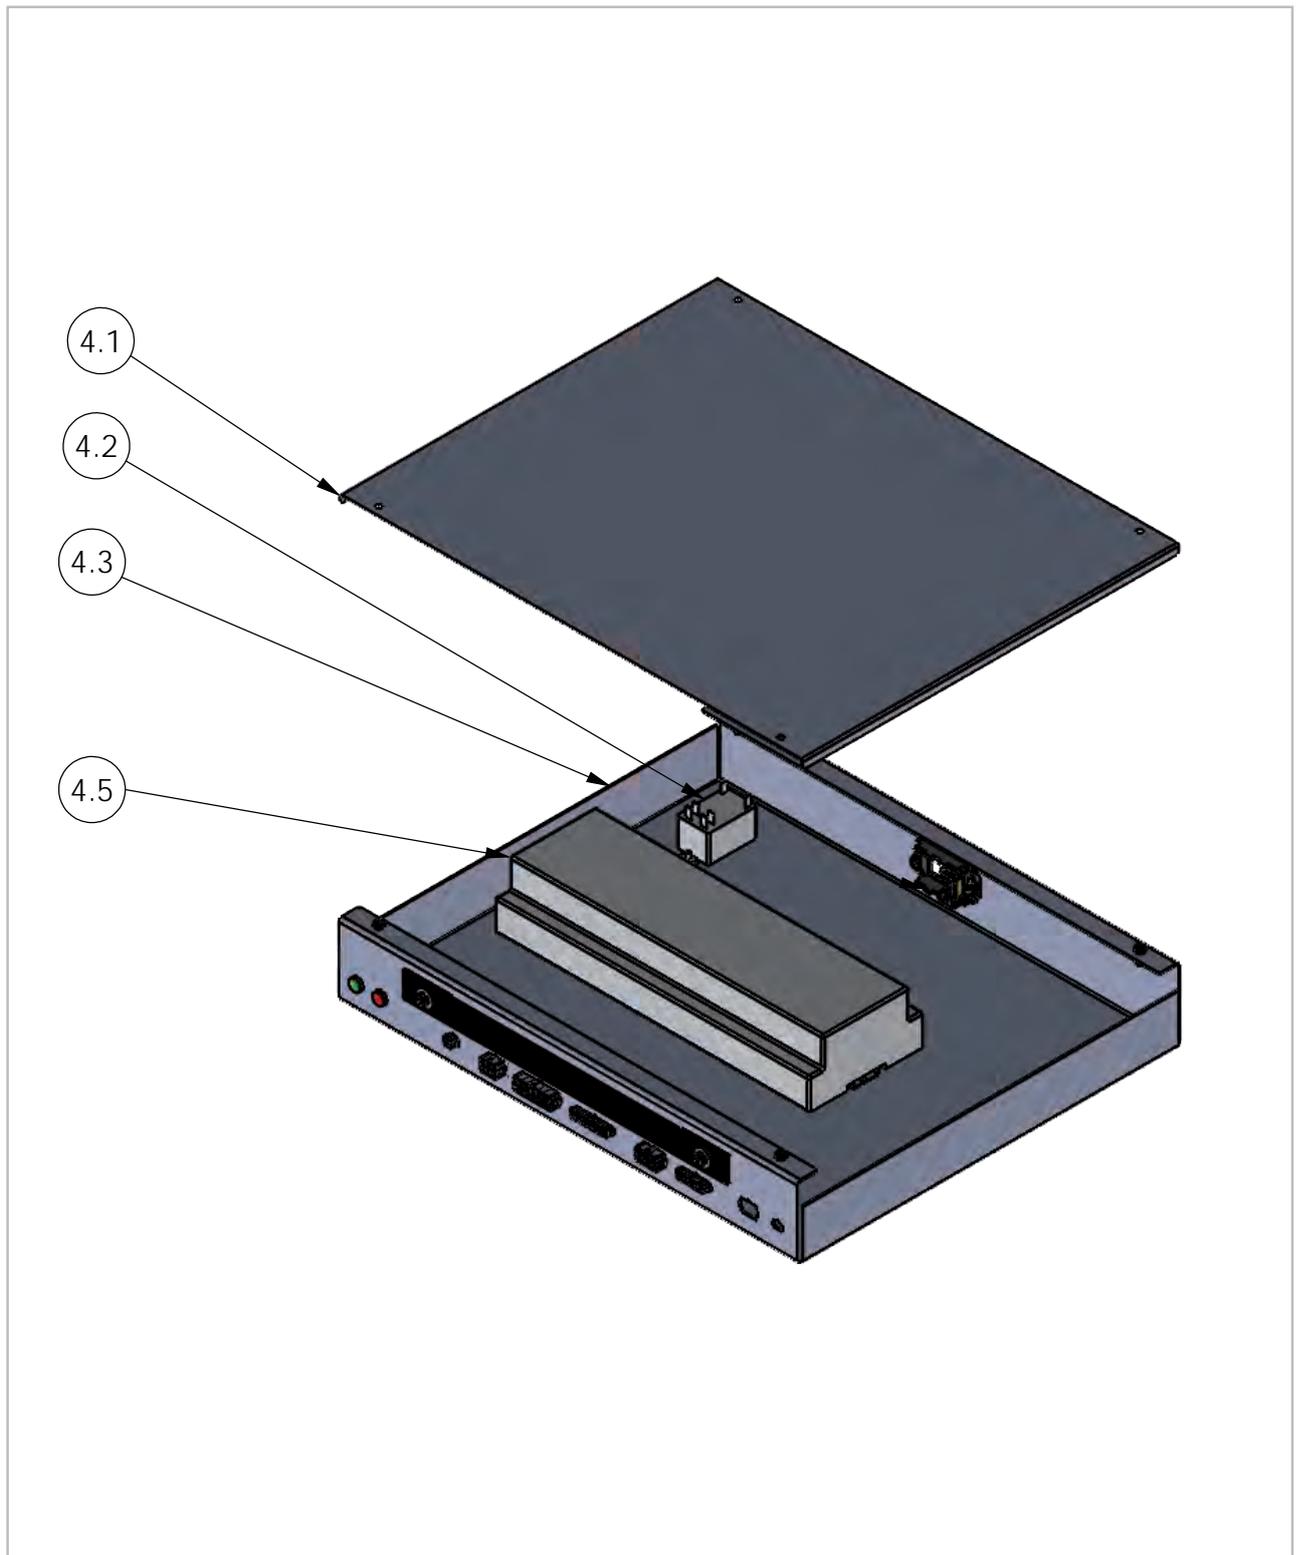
Explosionszeichnung Elektromodul MEL 35
